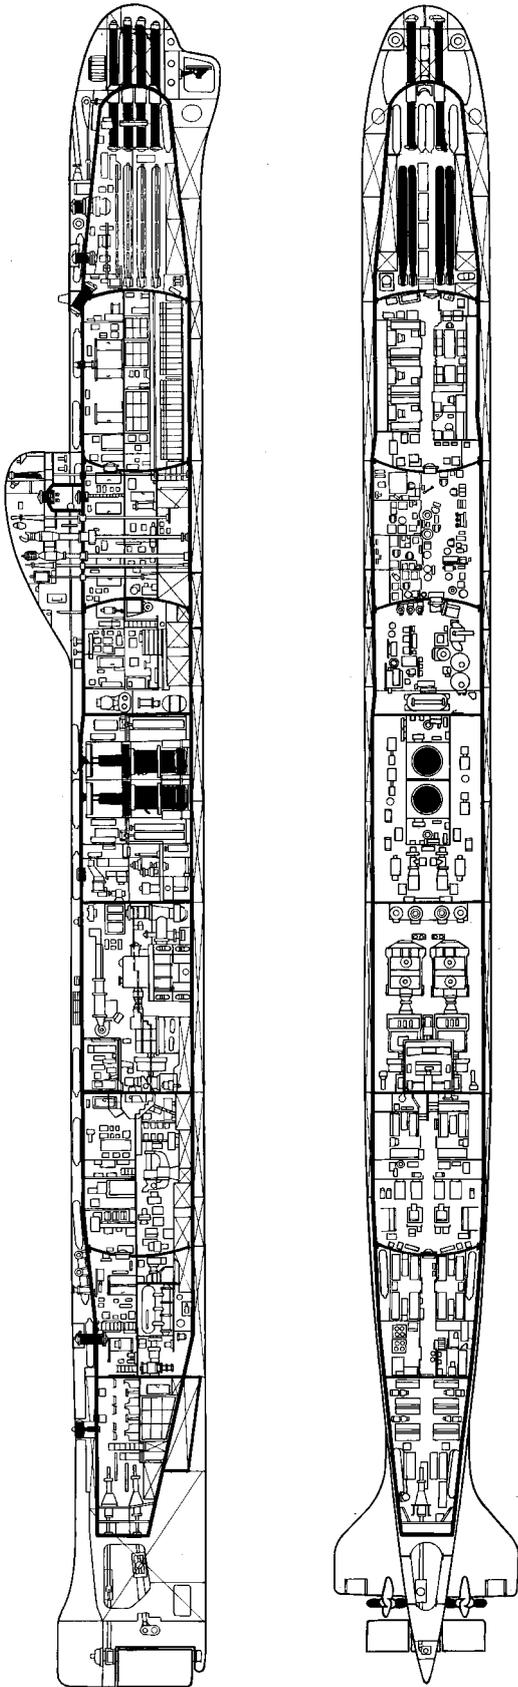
Продольный разрез и план АПЛ пр. 627А
